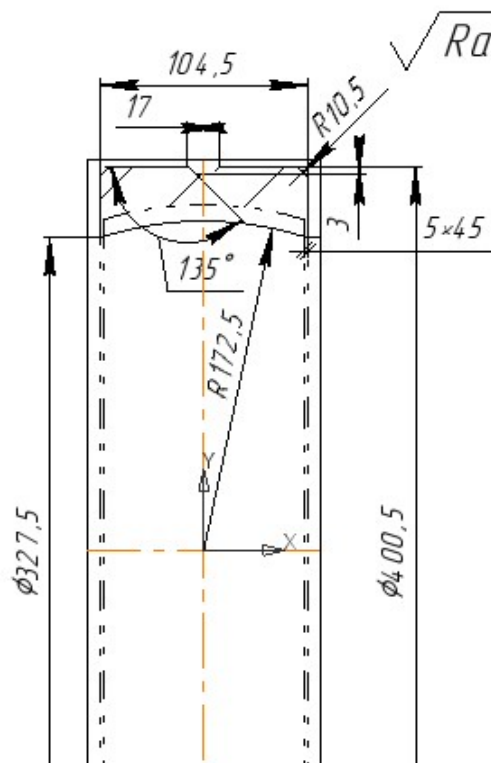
Креслення заготовки після токарної обробки на верстаті ПАБ350
